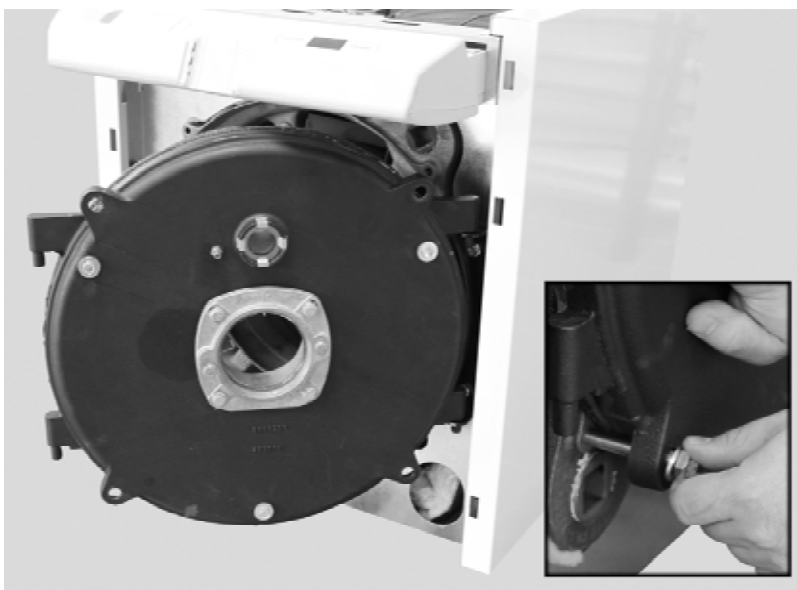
Accrocher la porte de la chaudière à la plaque charnière et la fixer au corps de la chaudière avec les vis fournies.
